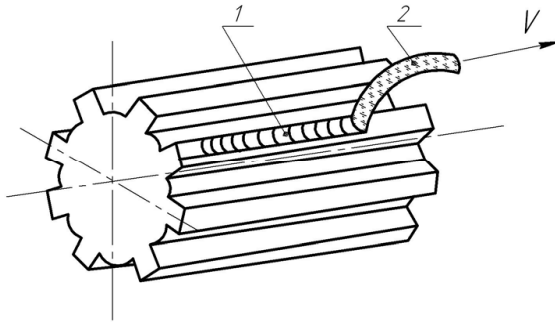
Схема продольной наплавки шлицевой поверхности детали:
